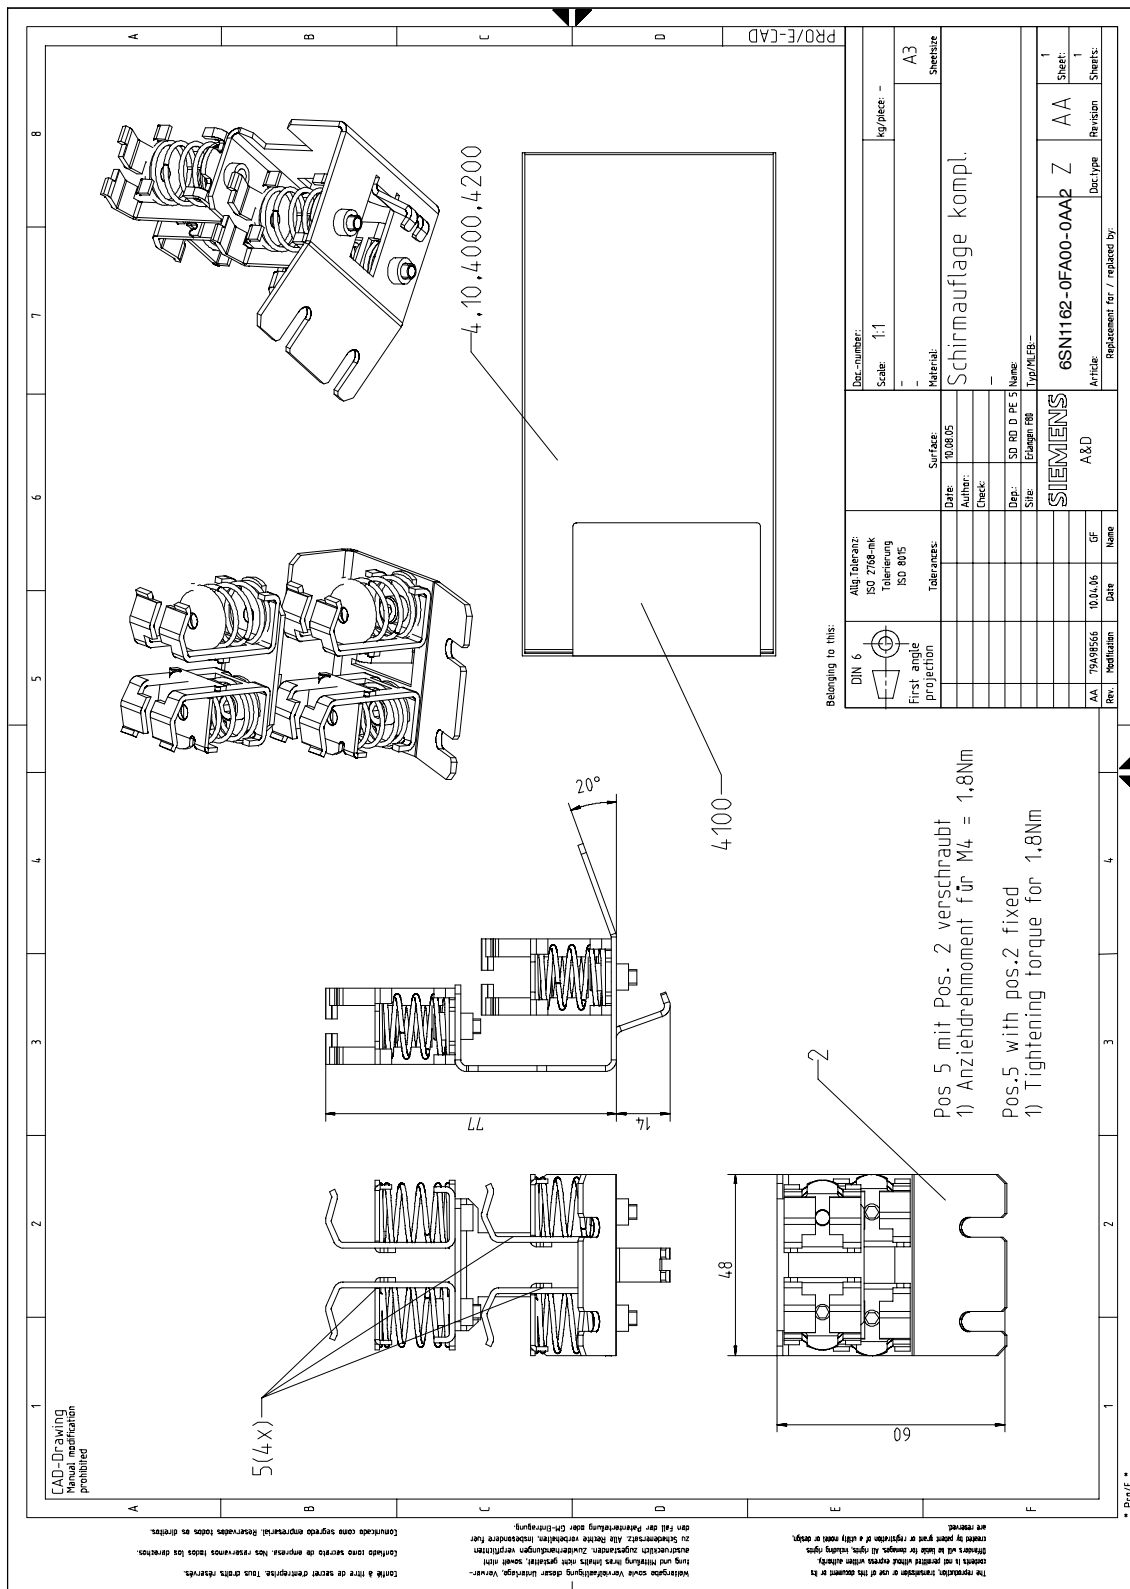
Connexion du blindage 6SN1162-0FA00-0AA2 (plan d'encombrement)
